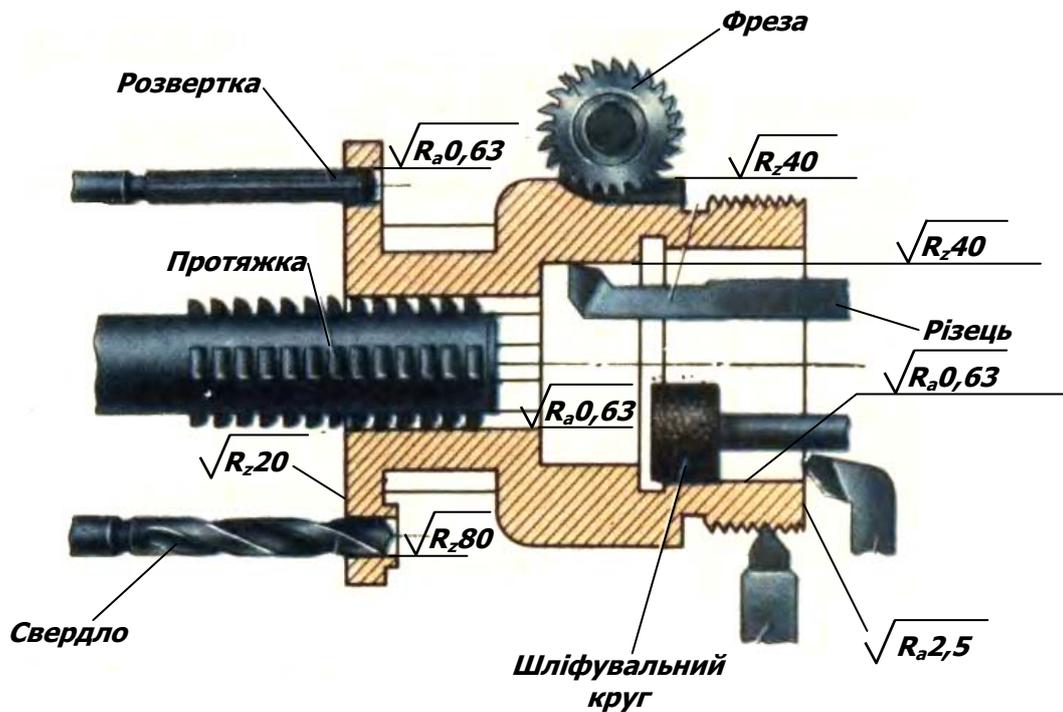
Шорсткість поверхнь сталі при різних методах обробки
